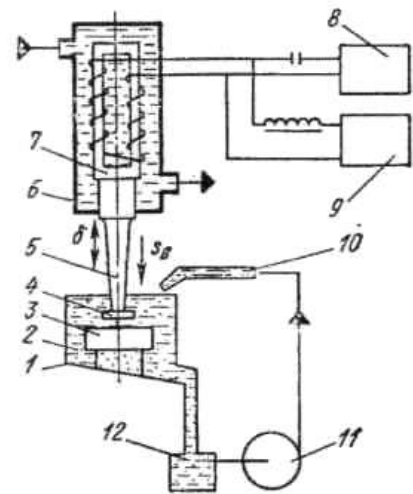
Схема устаткування для ультразвукової обробки.
